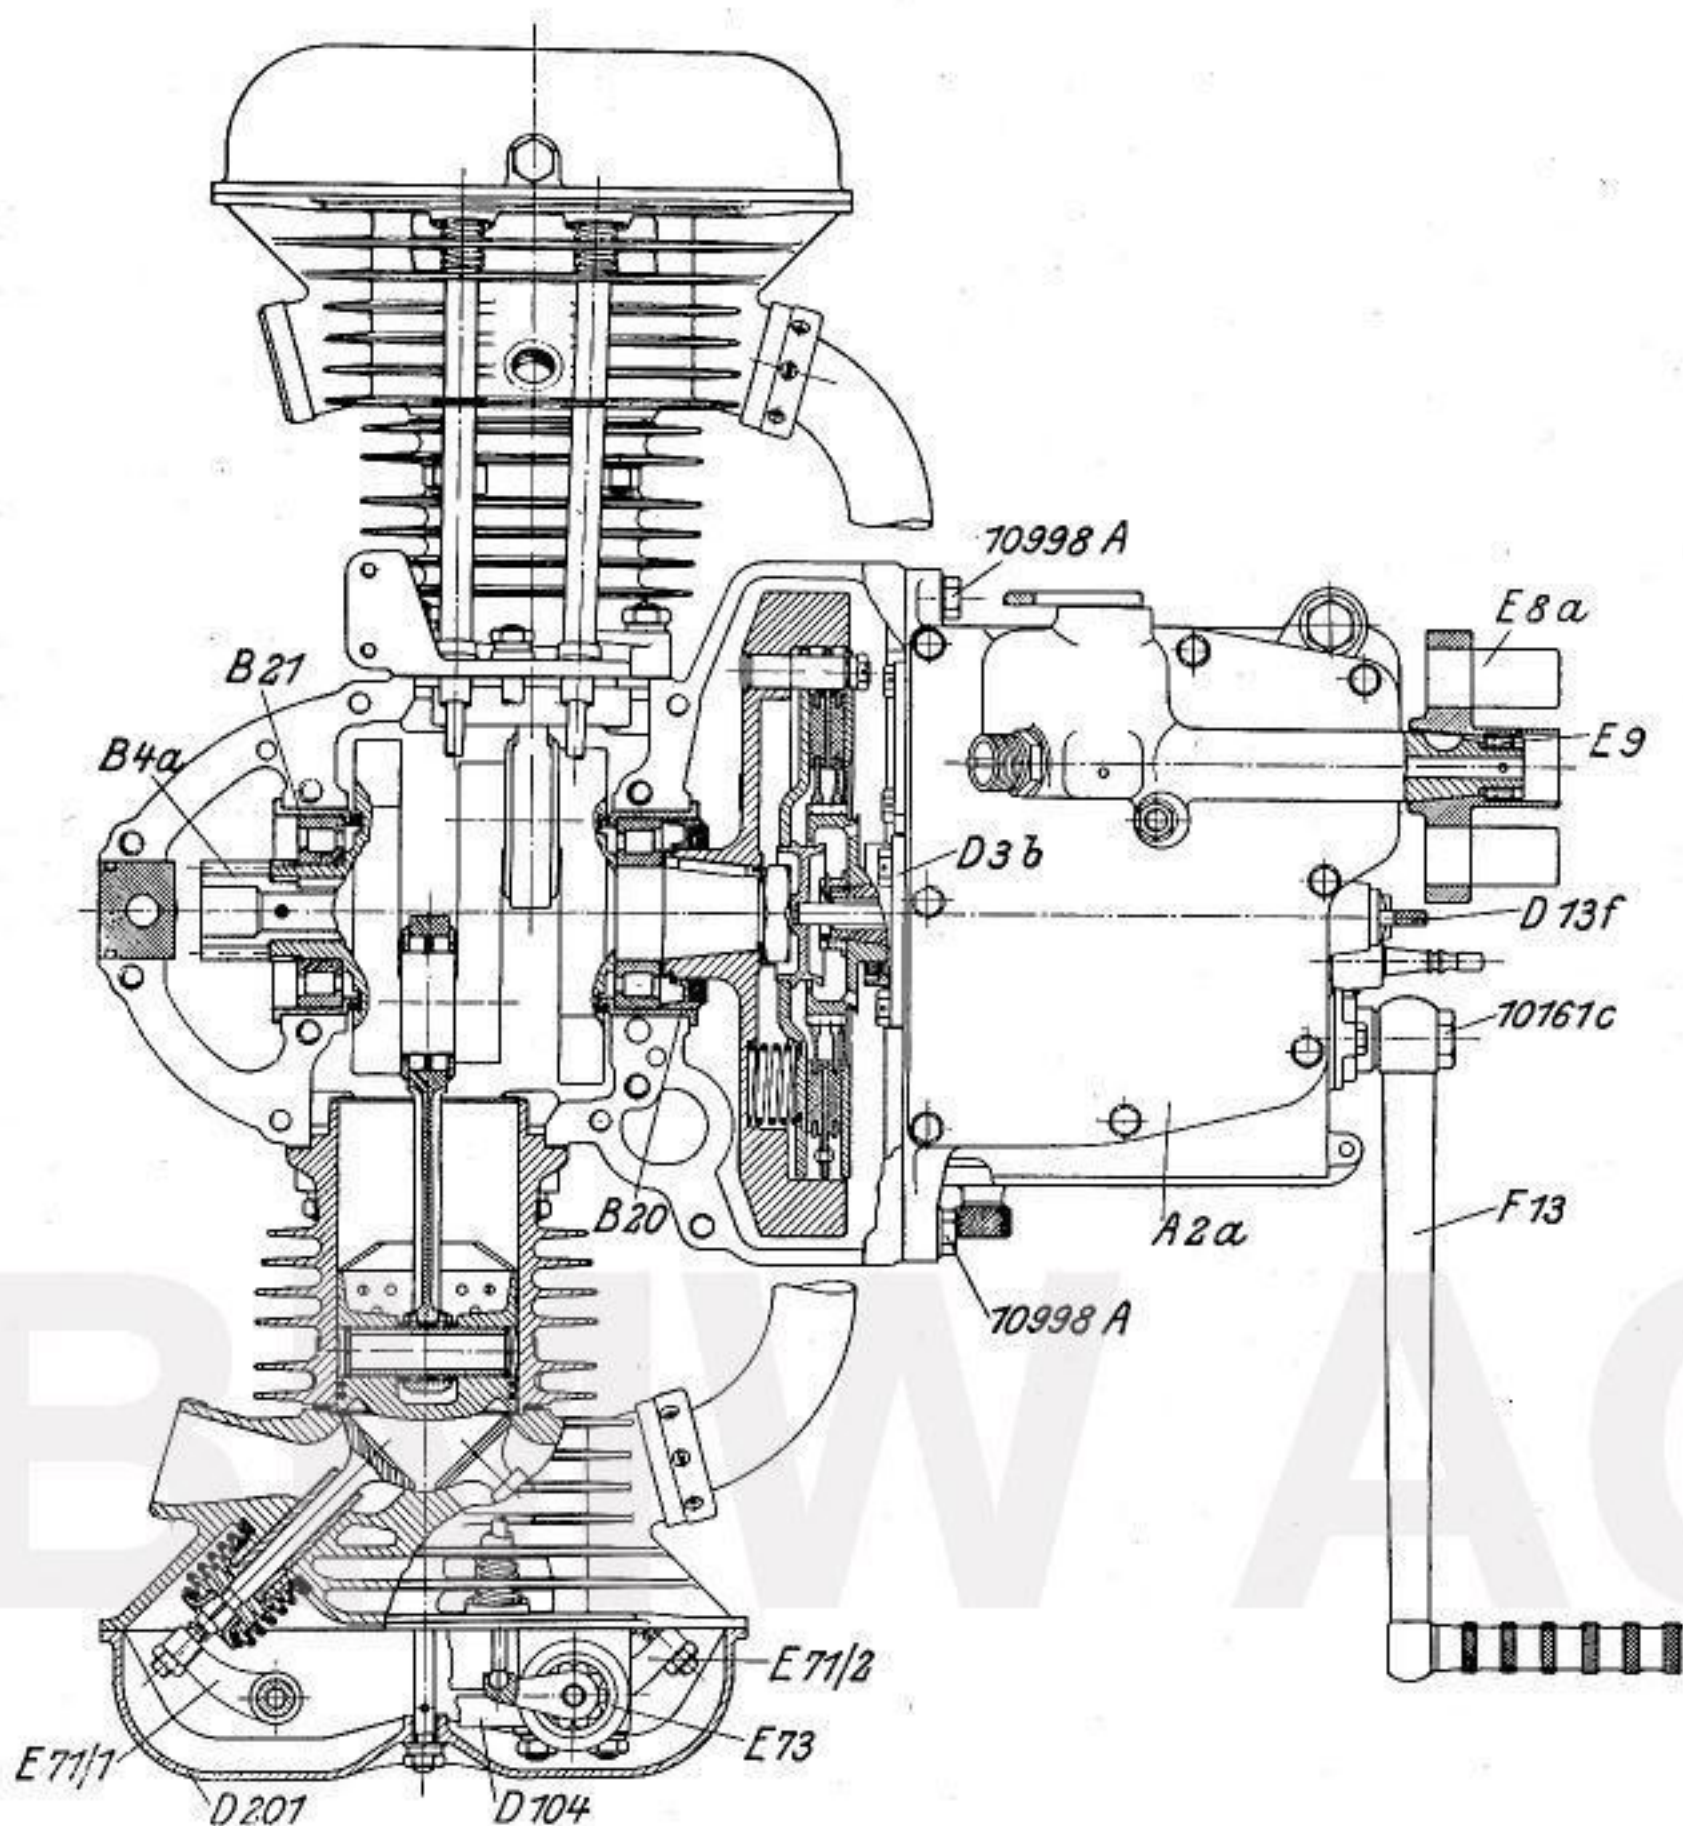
Sportmotor mit teilweiseem Horizontalschnitt durch die Zylindermittle
